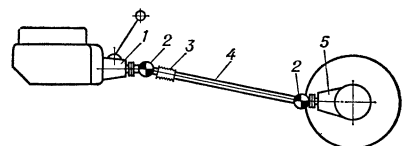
Схема карданной передачи автомобиля: 1 — коробка передач; 2 — кардан; 3 — скользящее шлицевое соединение; 4 — карданный вал; 5 — главная передача.
